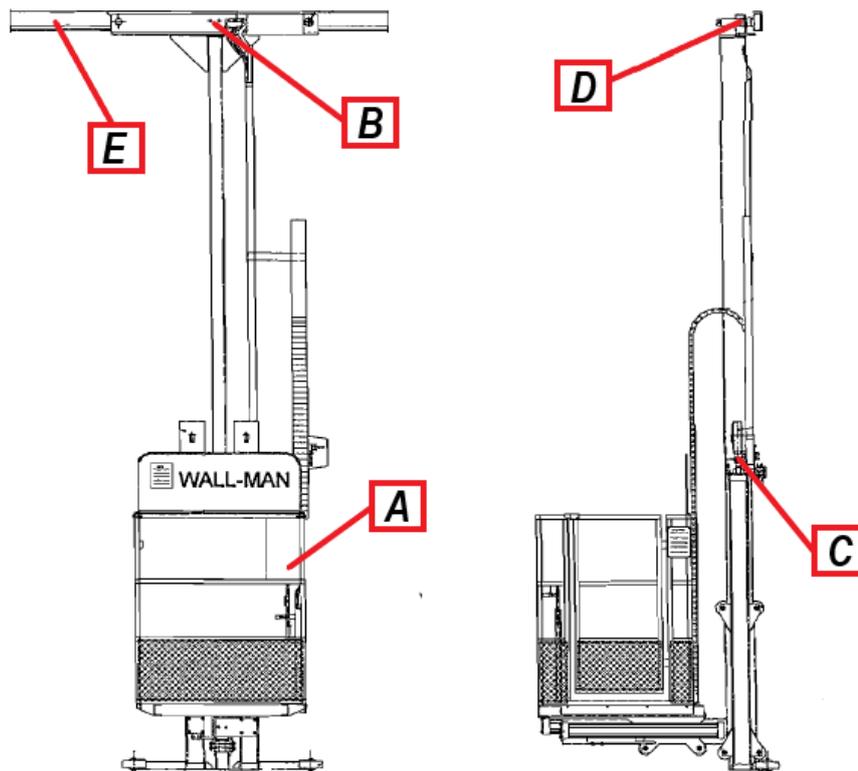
Plano de la plataforma de elevación Wall-Man.
